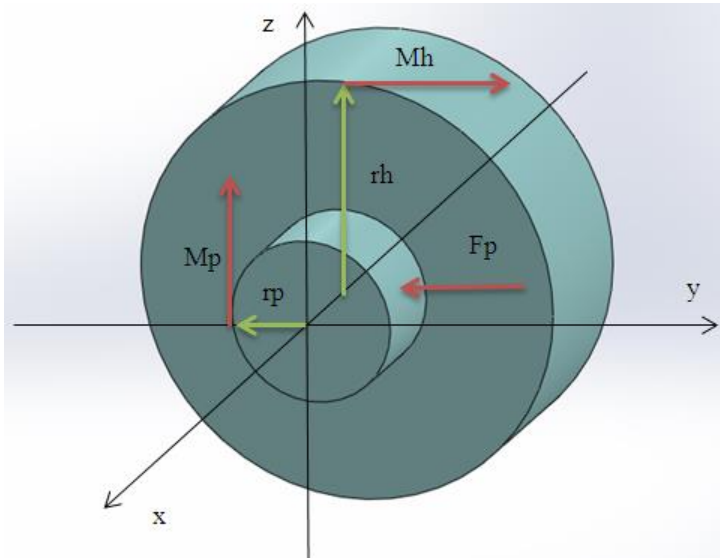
Cargas de torsión y de flexión presentes en la herramienta de soldadura
